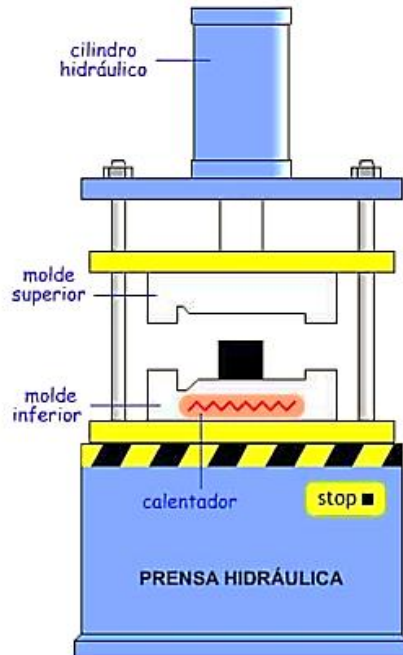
Prensa del moldeo por compresión con sus diferentes partes.
